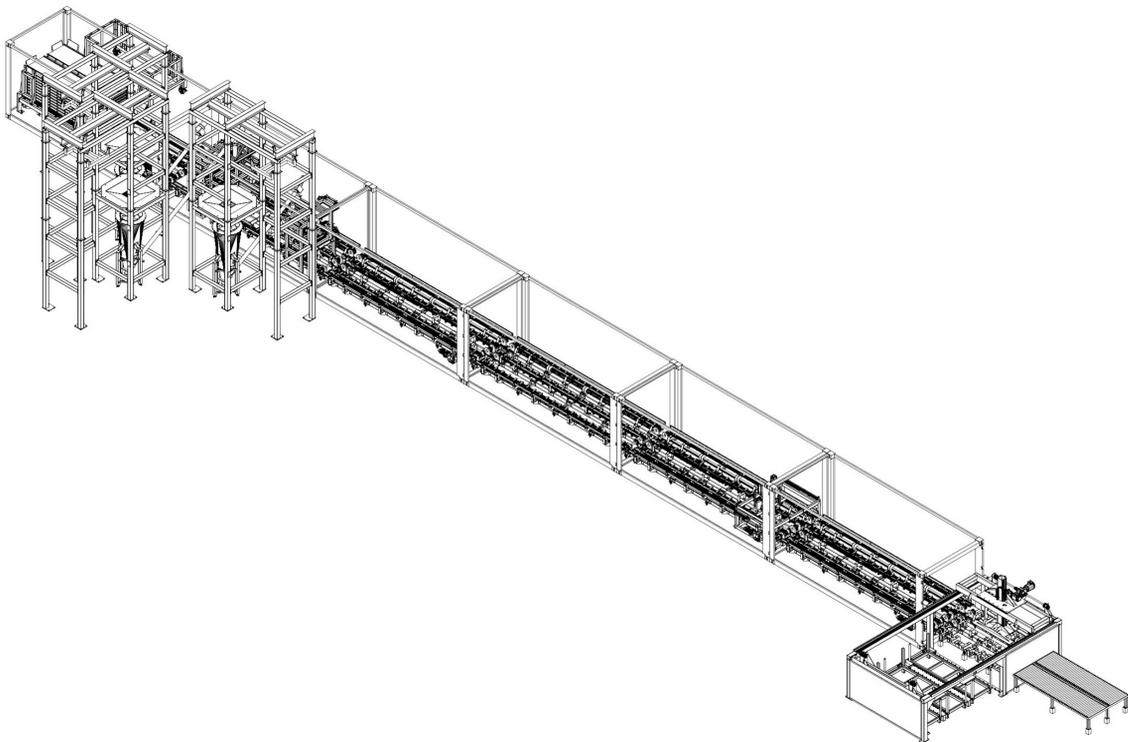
Mobiles Produktionslayout in Containern © Gtecz Engineering GmbH
